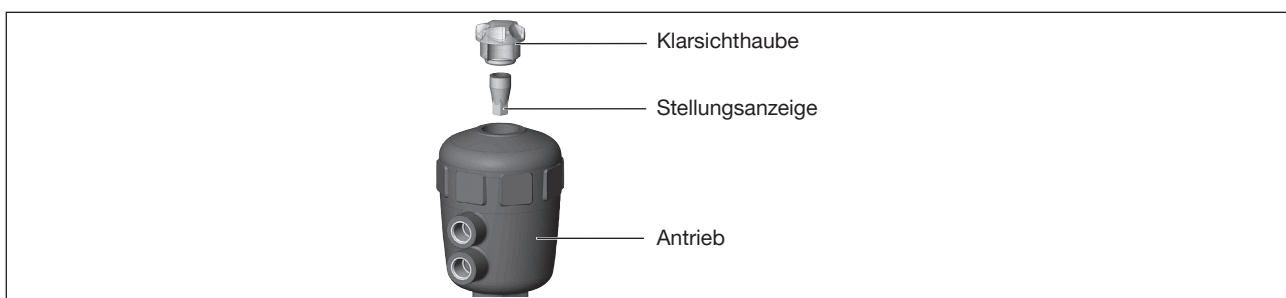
Schaltspindel montieren (1), externe Steuerluftführung
